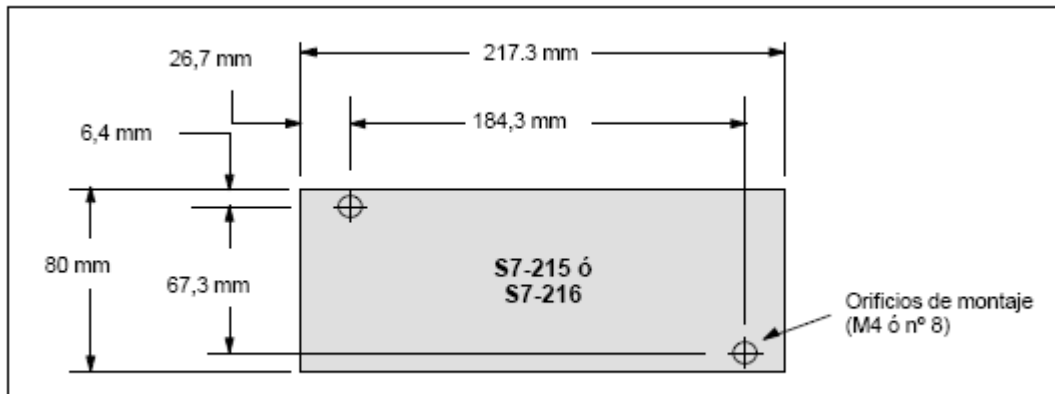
Dimensiones de montaje para una CPU S7-215 ó 216.
